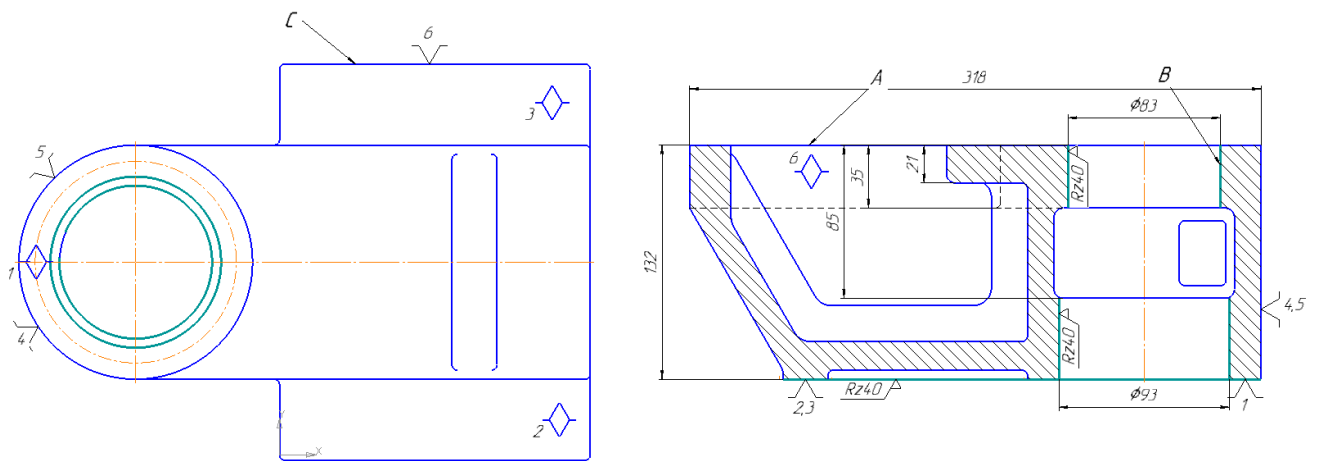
Схема базування та закріплення заготовки на операції 015
